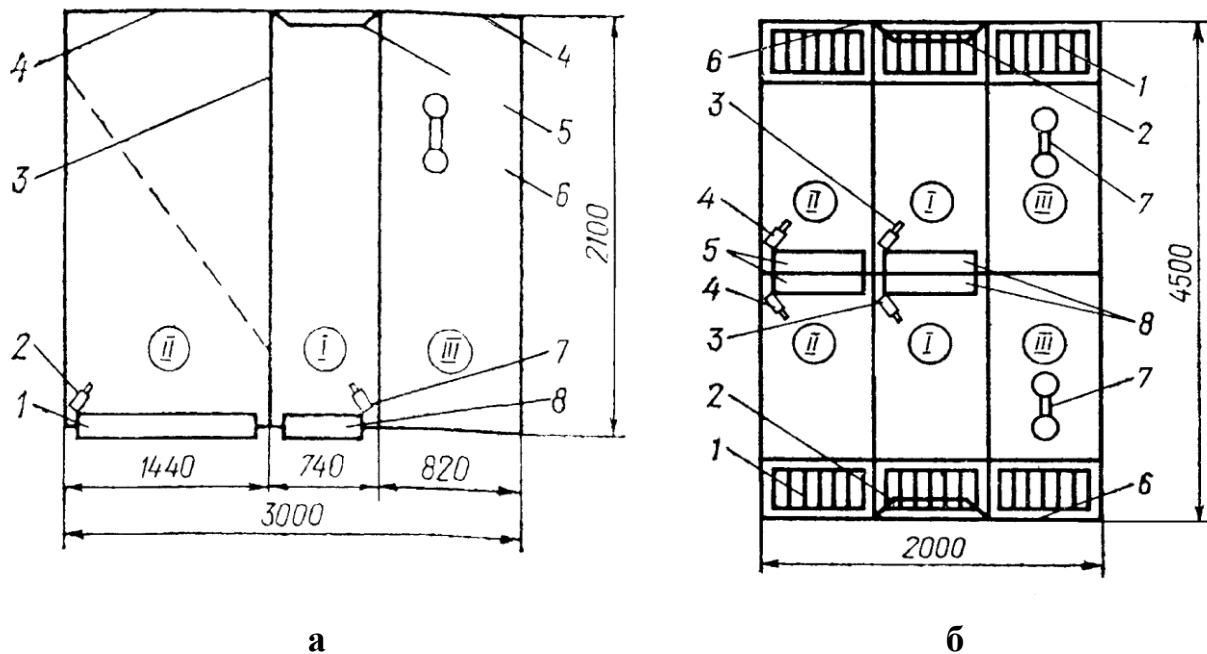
Схема станкового обладнання : а – ОСМ - 60; б – ССД - 2
